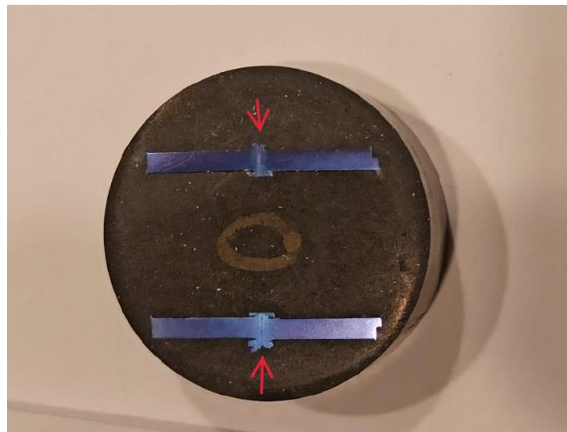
Sección longitudinal de la probeta 0, las flechas indican las zonas soldadas en la pared del tubo.
